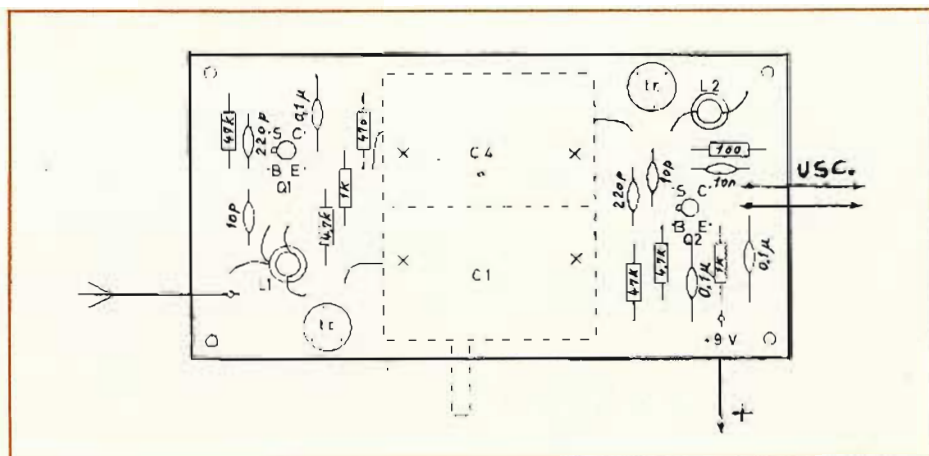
Il circuito stampato del preselettore visto dal lato componenti.
